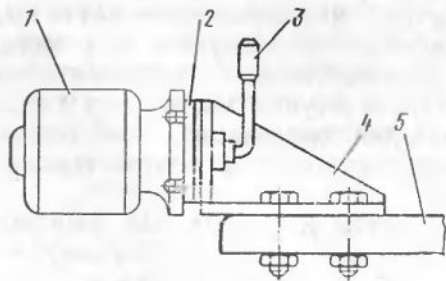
Приспособление для бестисковой сборки или разборки агрегата
